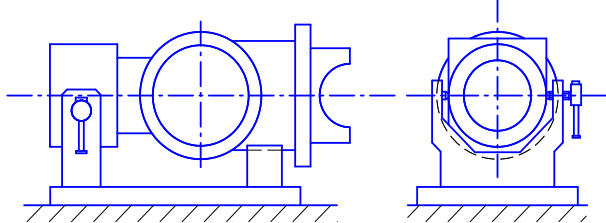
Схема приспособления для ориентации, установки и крепления картера заднего моста автомобиля
